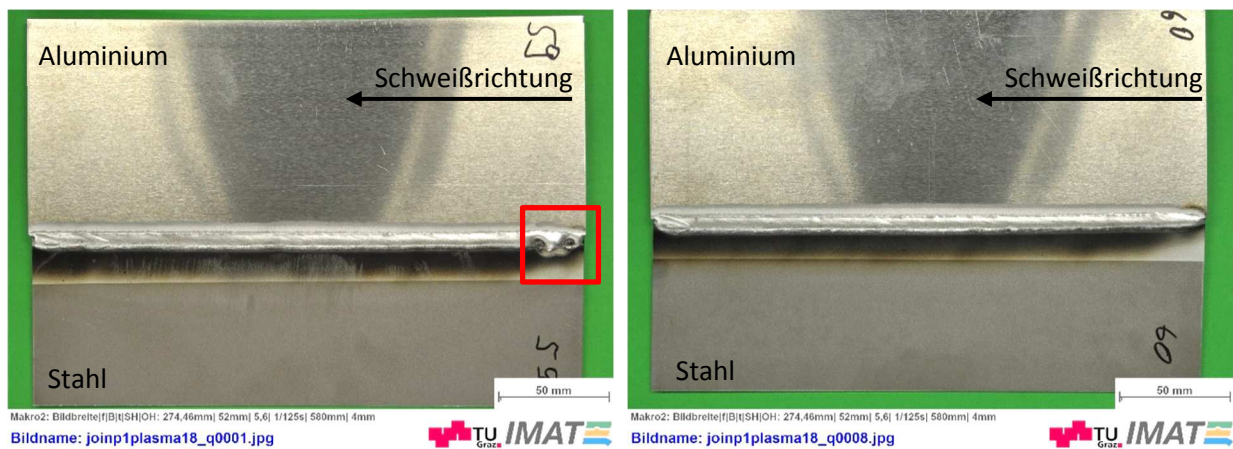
Schweißnähte der Hauptversuche 59 (links) und 60 (rechts); Bindefehler rot markiert
